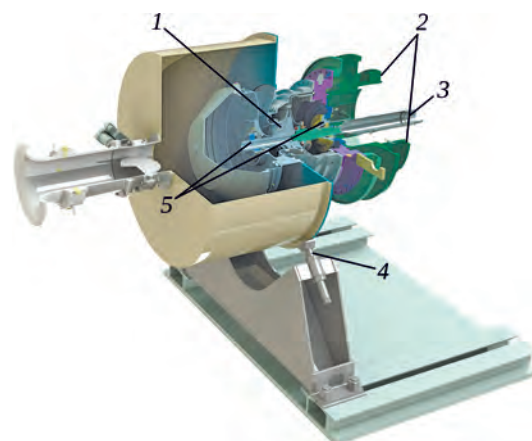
Общий вид (разрез) центробежного компрессора в составе испытательной установки:
